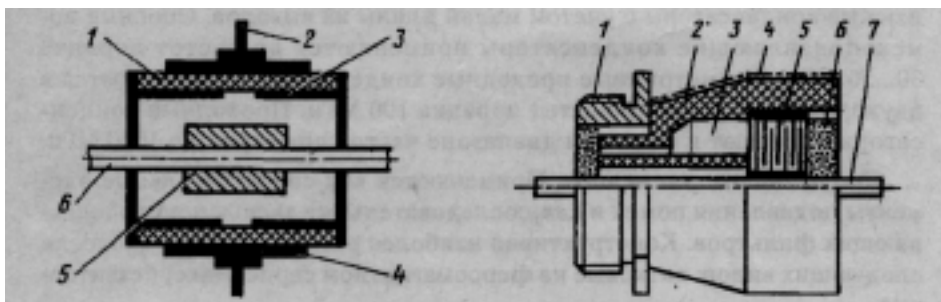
Конструкция керамического проходного фильтра типа Б7:
